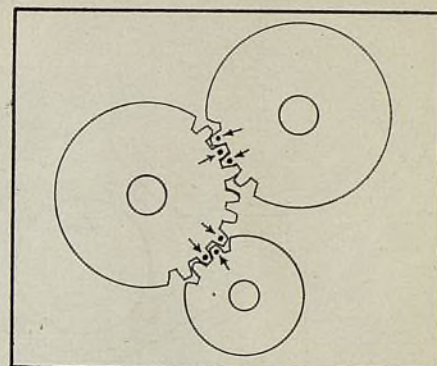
Cuando se emplea un engranaje loco, los engranajes de distribución se marcan como se indica aquí. Estas marcas aseguran un correcto montaje.
